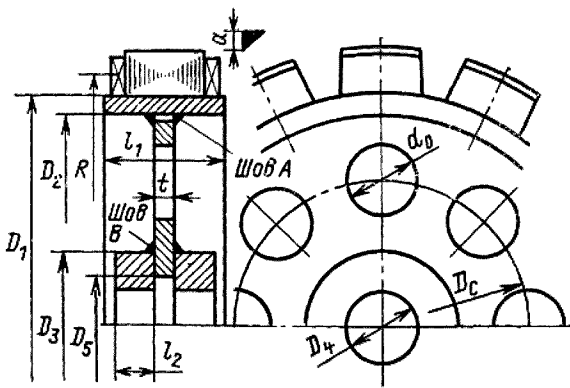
К расчету ротора в виде сварного магнитного колеса
